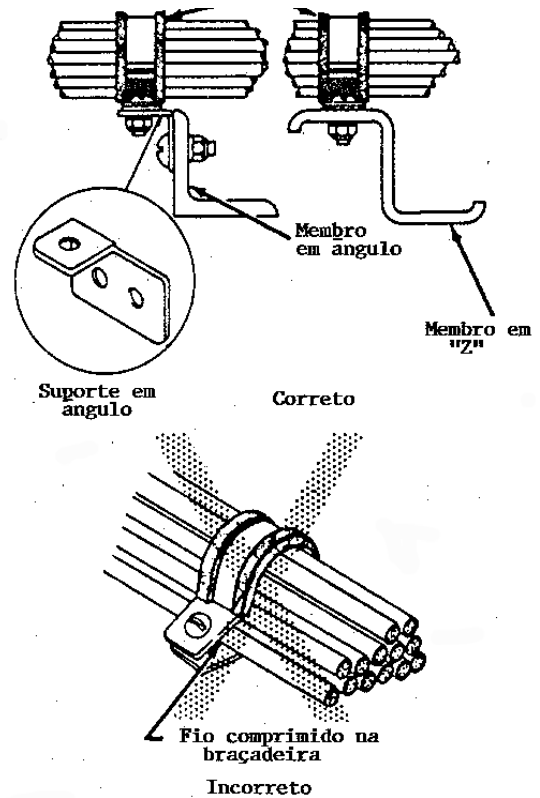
Montagem da braçadeira de cabo na estrutura.
